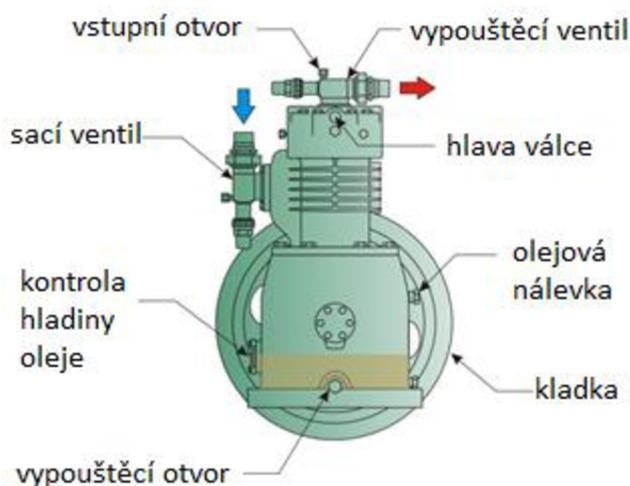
Jednotlivé díly semihermetického kompresoru [9]
